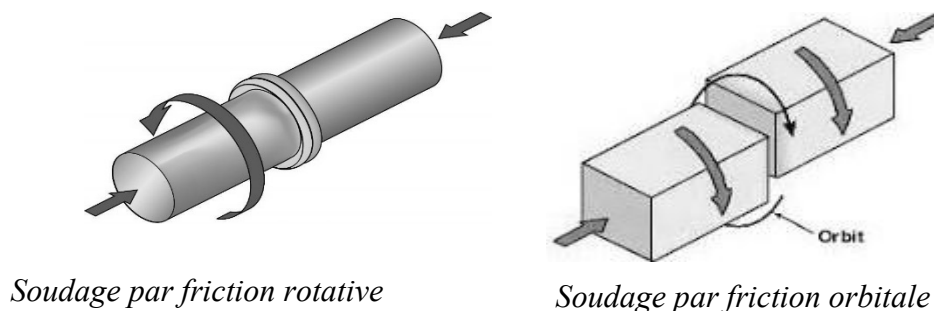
Soudage par friction rotative et orbitale.
